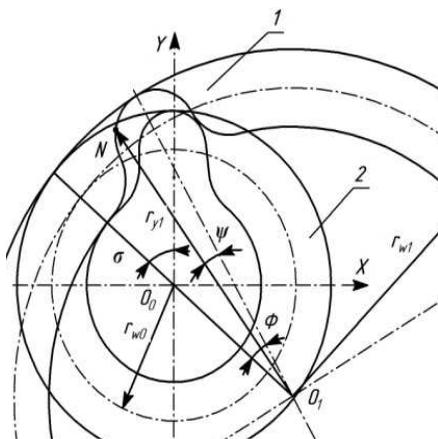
Определение положения впадины колеса с внутренними зубьями 1 относительно зуба долбяка 2.
